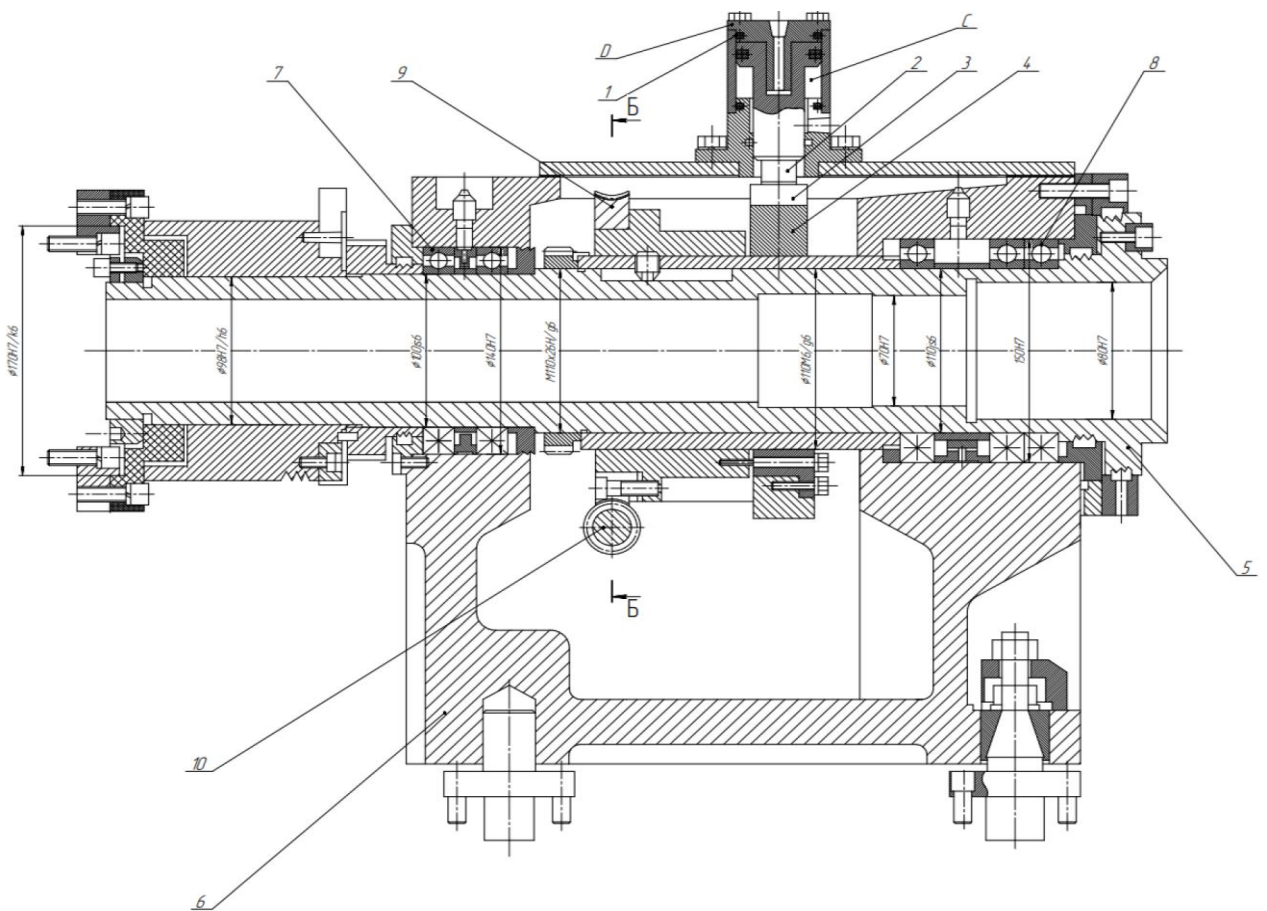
Шпиндельна бабка токарно-револьверного багатоопераційного верстату з ЧПК мод. 1П420ПФ40 з механізмом фіксації шпинделя
